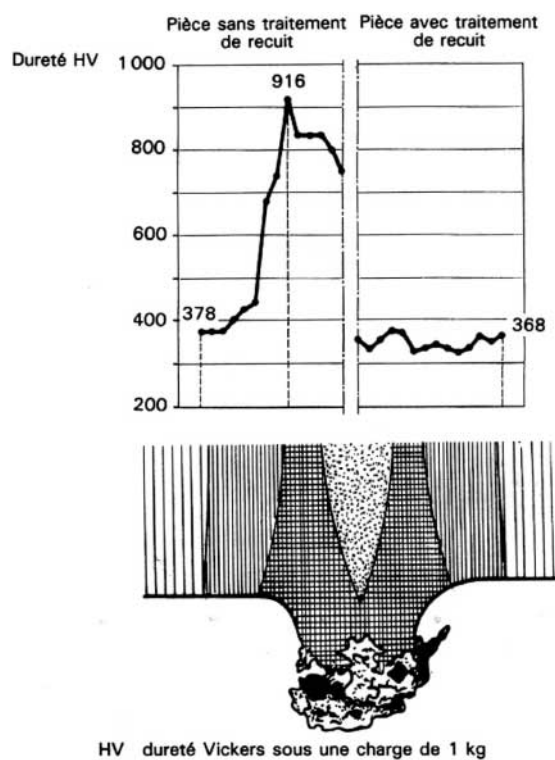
Soudage en bout : dureté d'une soudure
